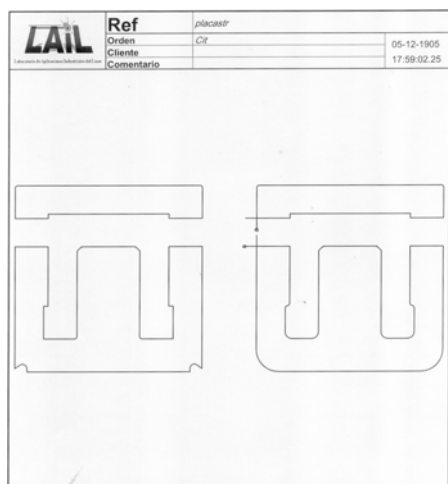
Diseño de piezas introducidas en el CNC, del láser.
